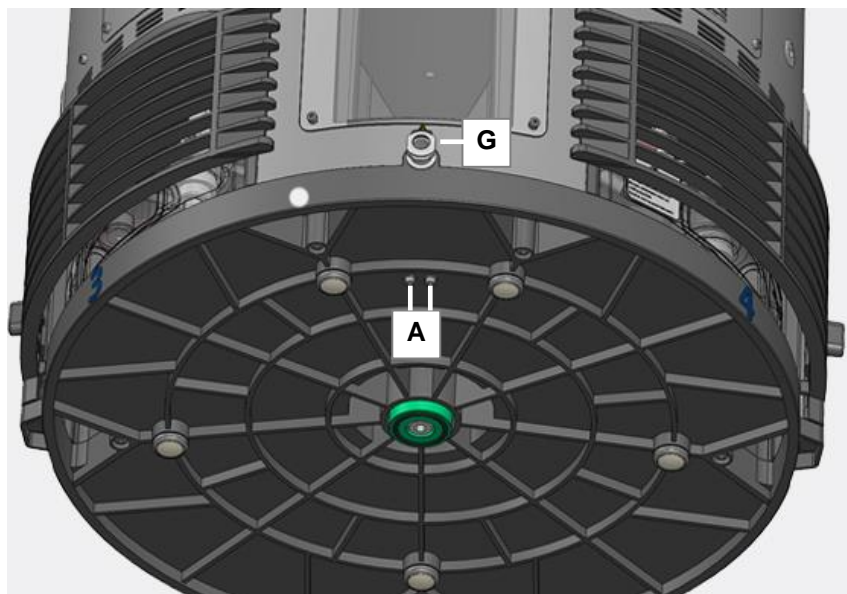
Vista inferior de la máquina con atornilladura
